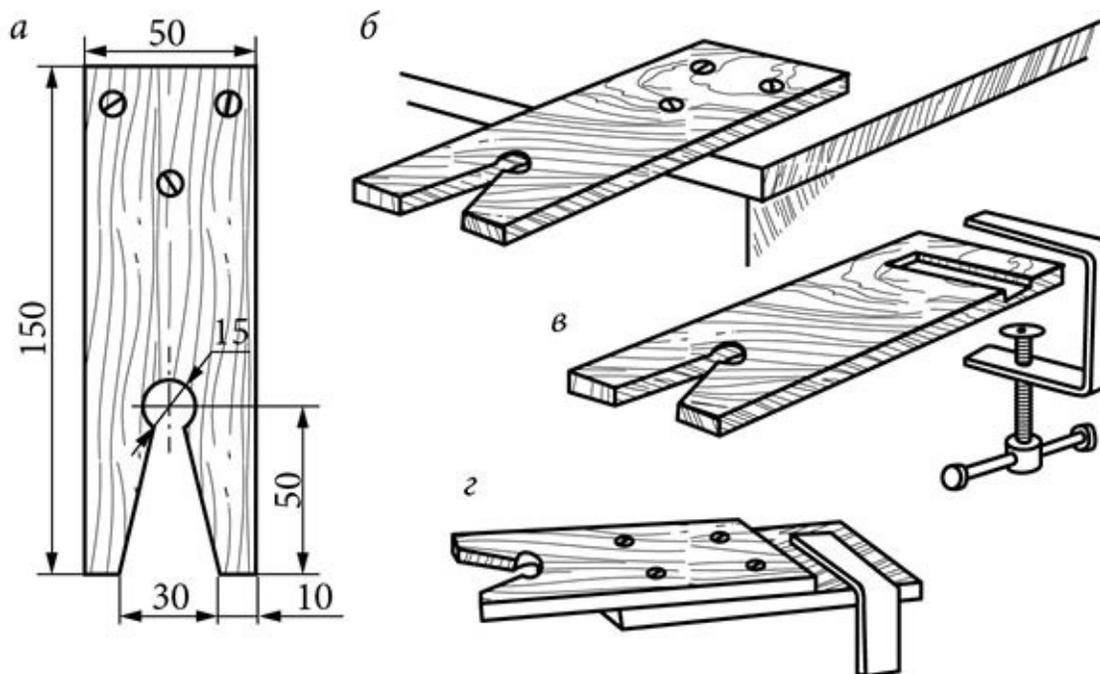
Выпиловочный столик: а – форма и основные размеры столика; б – крепление выпиловочного столика к верстаку с помощью шурупов; в, г – варианты крепления столика с помощью металлической струбцины.
